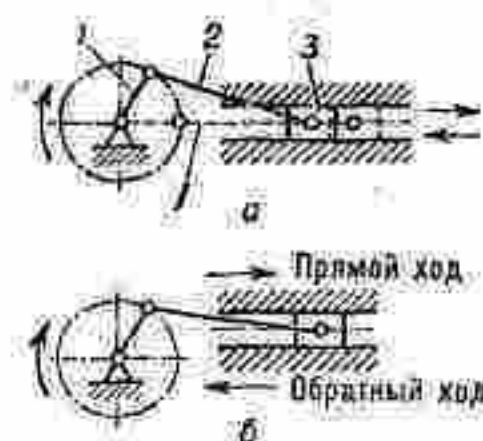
Кривошипно-ползунный механизм (1 — мёртвое положение): а — центральный; б — смещённый; 1 — кривошип; 2 — шатун; 3 — ползун.
